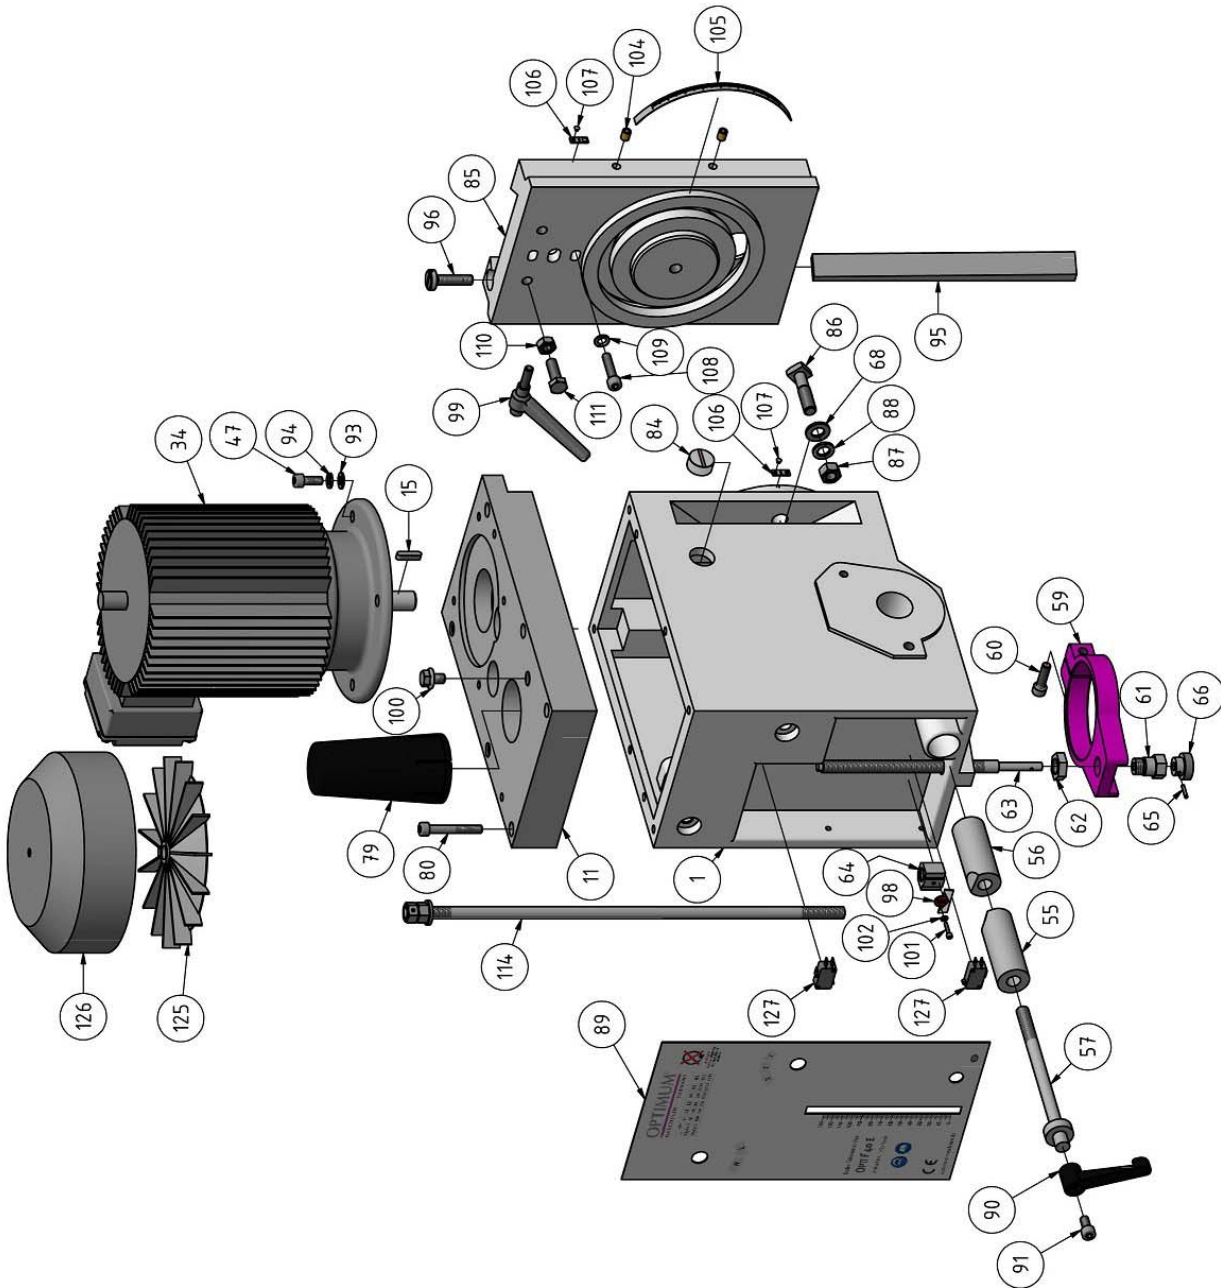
Fräskopf 6 von 6 - Milling head 6 von 6
